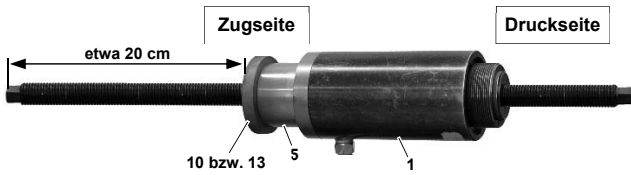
Radnabe aufstecken. Druckring und Aufnahmeadapter montieren. Spannmutter aufschrauben.
